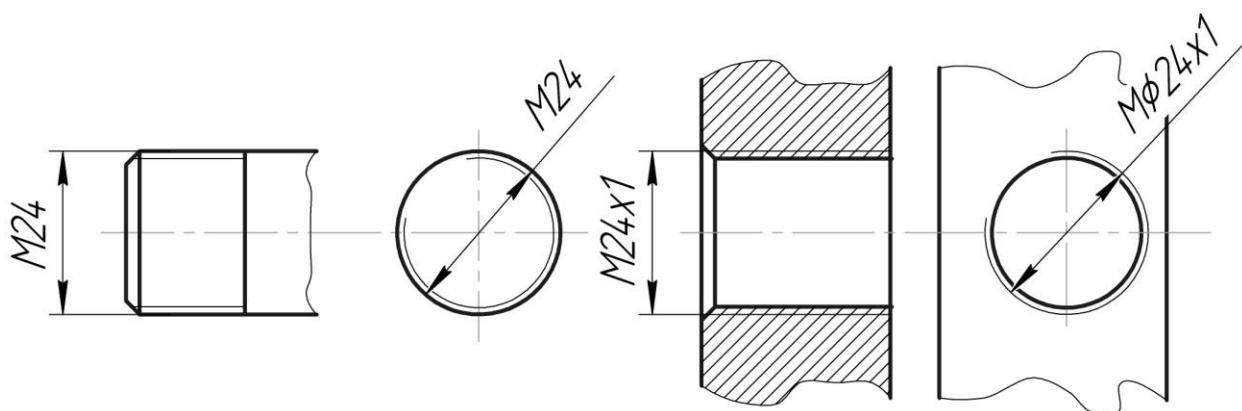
Обозначение метрической резьбы на чертеже детали:
